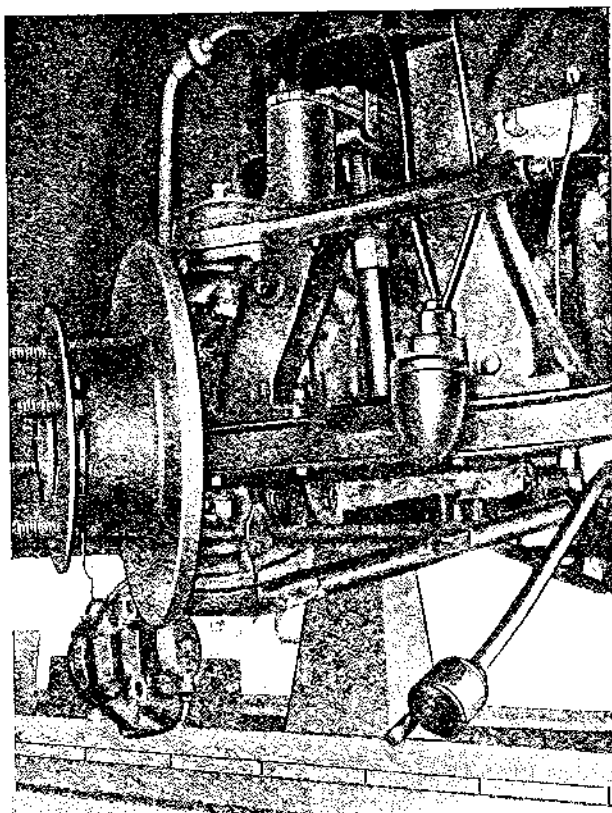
/5 - Mise en place outil 8043111 pour charger le demi-ressort.
